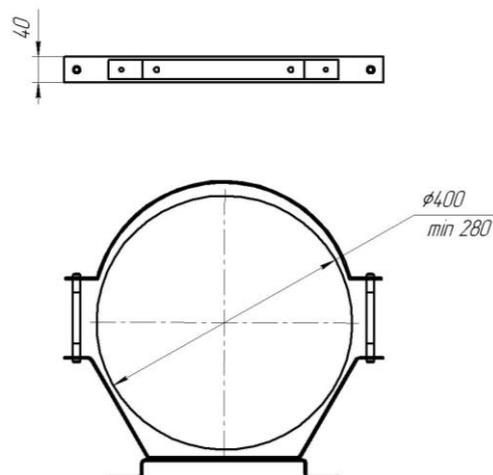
Элементы крепления на опоры круглого сечения
